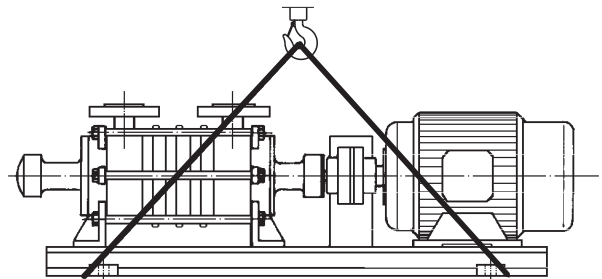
Hebezeug befestigen an Pumpenaggregat mit Grundplatte
